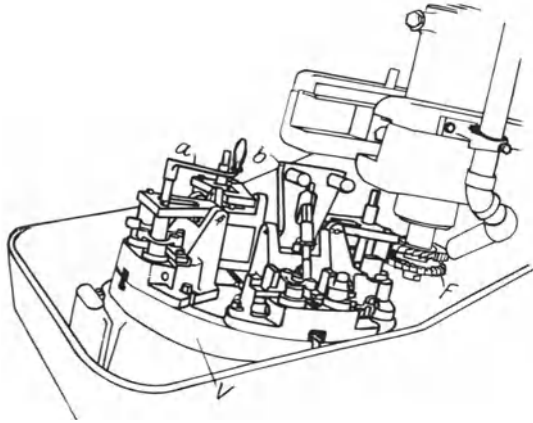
Das Fräsen auf einer 4-Stationen-Vorrichtung.
